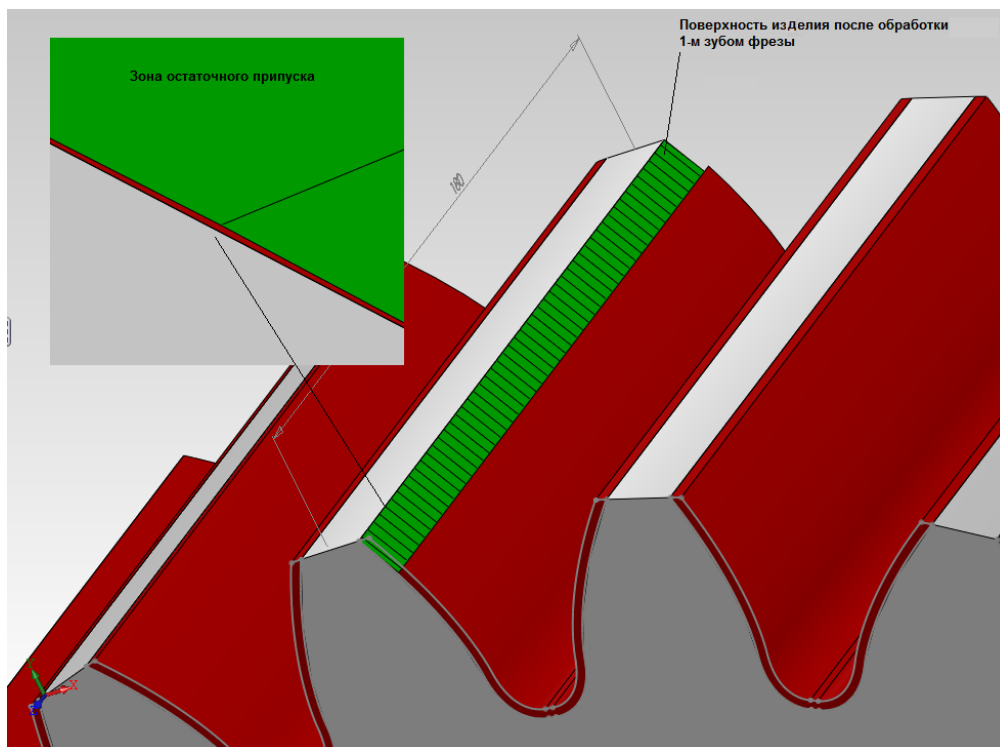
Формообразование поверхностного слоя одним зубом зубообрабатывающей фрезы
